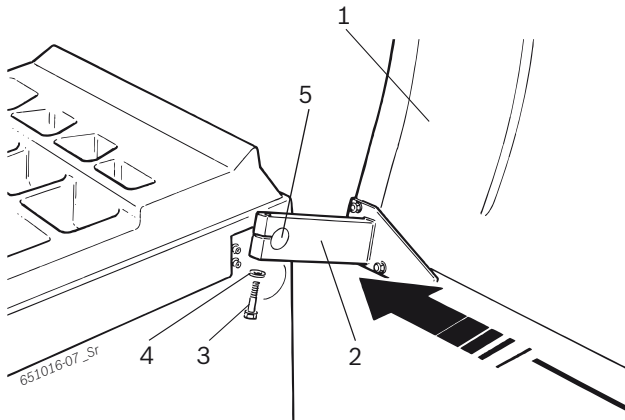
Montaggio della calotta di protezione ruota sulla MT 788
